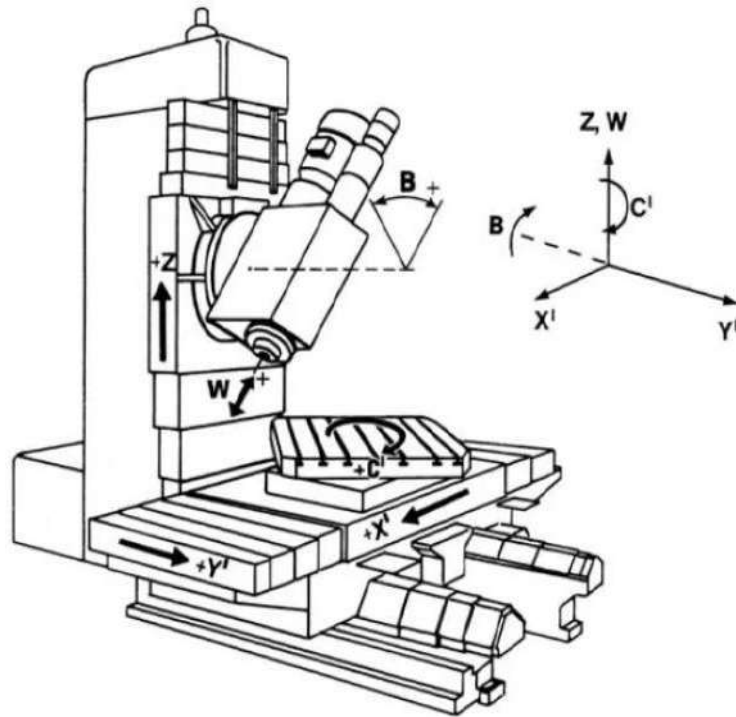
Фрезерний верстат з можливістю кутової обробки
